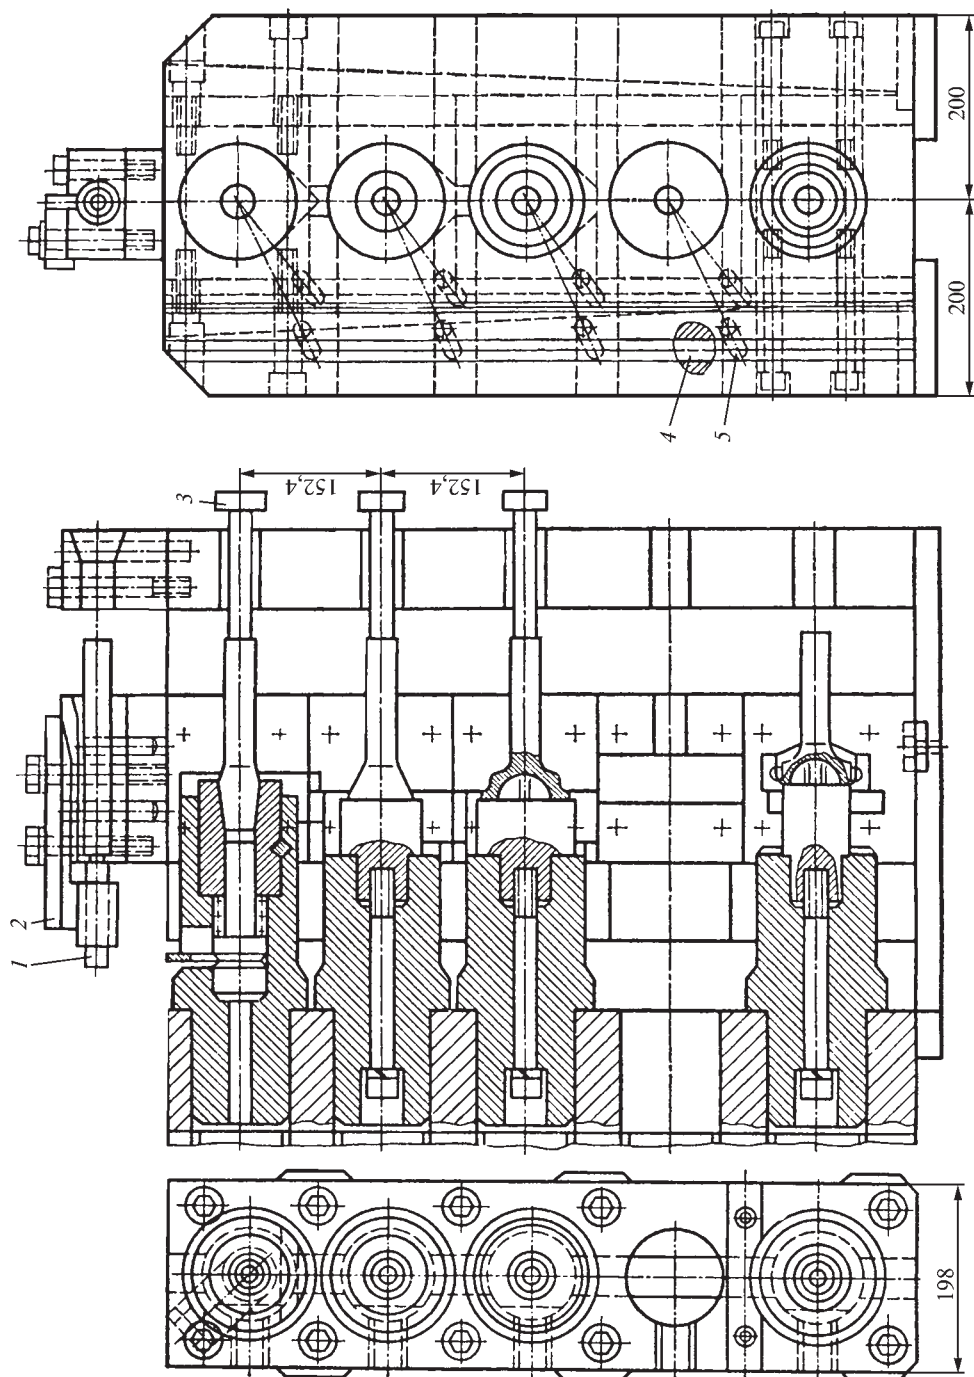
Штампы для автоматической поковки концов карданного вала за четыре перехода
